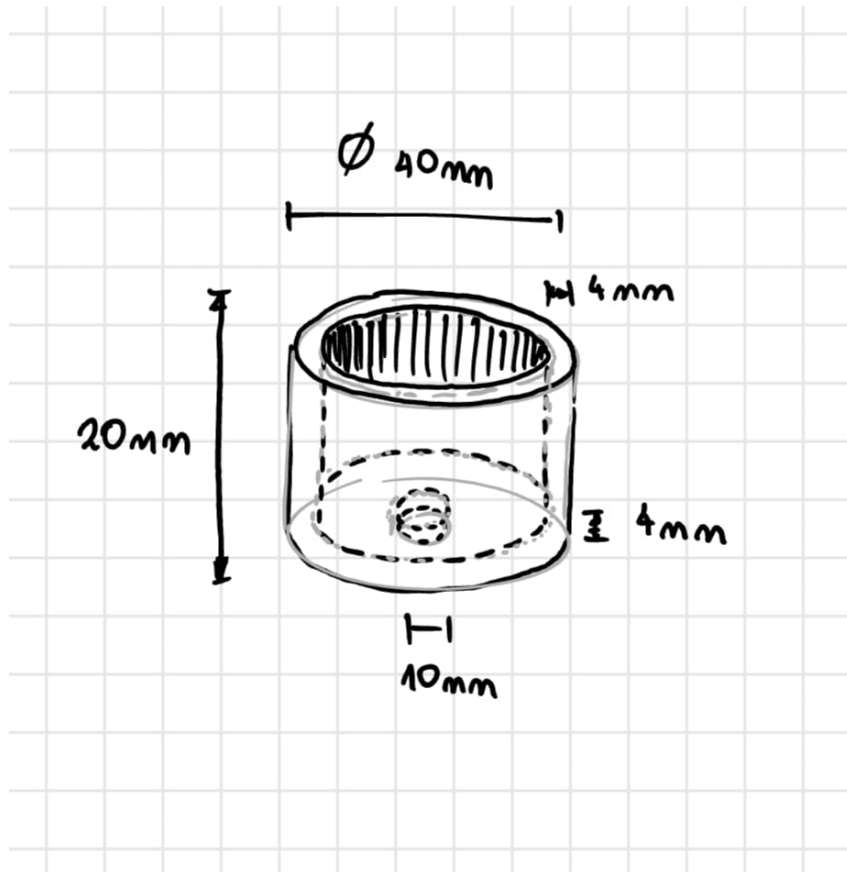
Plano de pieza a fabricar. Fuente: elaboración propia
